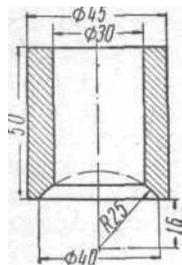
Оправка для завальцовки корпуса шарового шарнира
